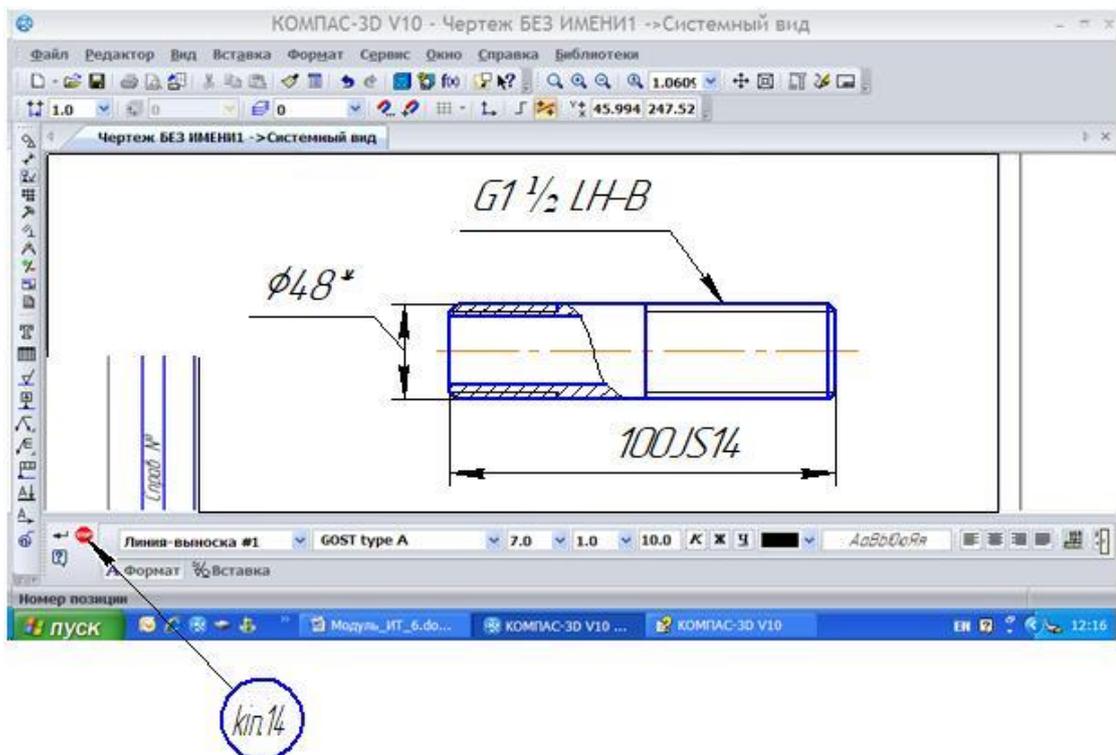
Фрагмент детали с обозначением трубной цилиндрической резьбы
